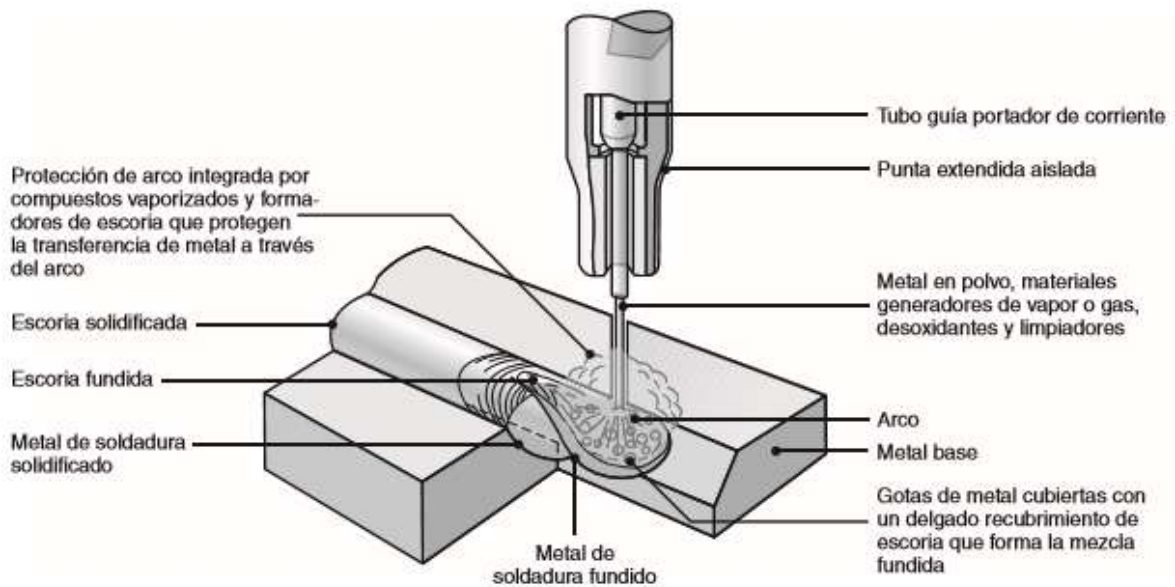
Esquema del proceso de soldadura FCAW [3]
